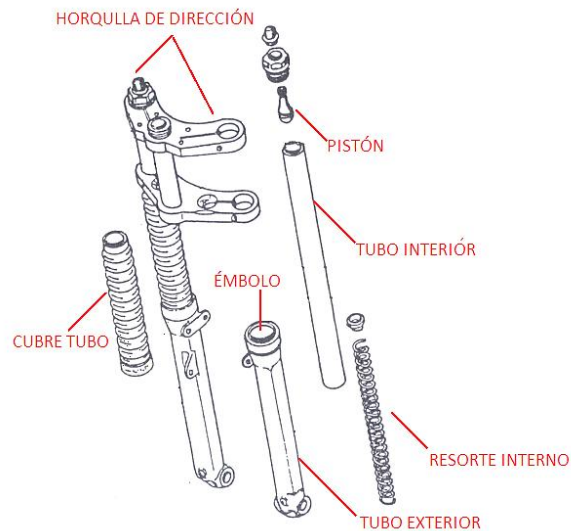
Despiece suspensión delantera del prototipo Moto-Oruga
